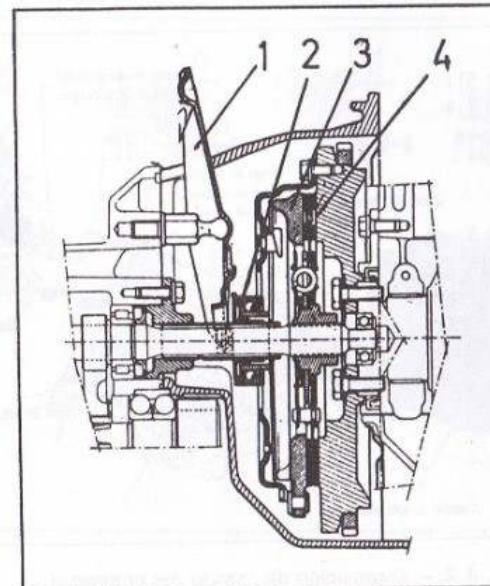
Emplazamiento del embrague sobre el motor.
